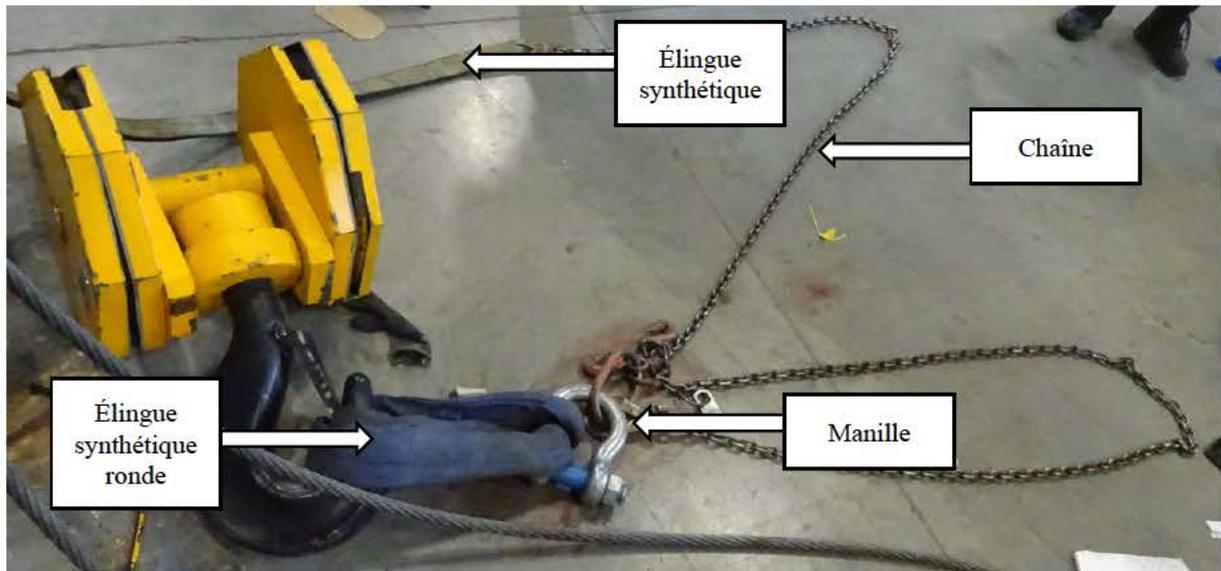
Moufle et accessoires utilisés pour l'assemblage
